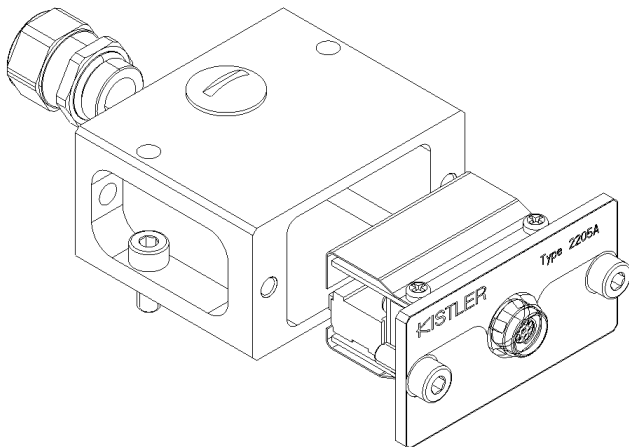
Einbau in Gehäuse mit Kabelverschraubung Typ 1417 für In-Line-Montage
